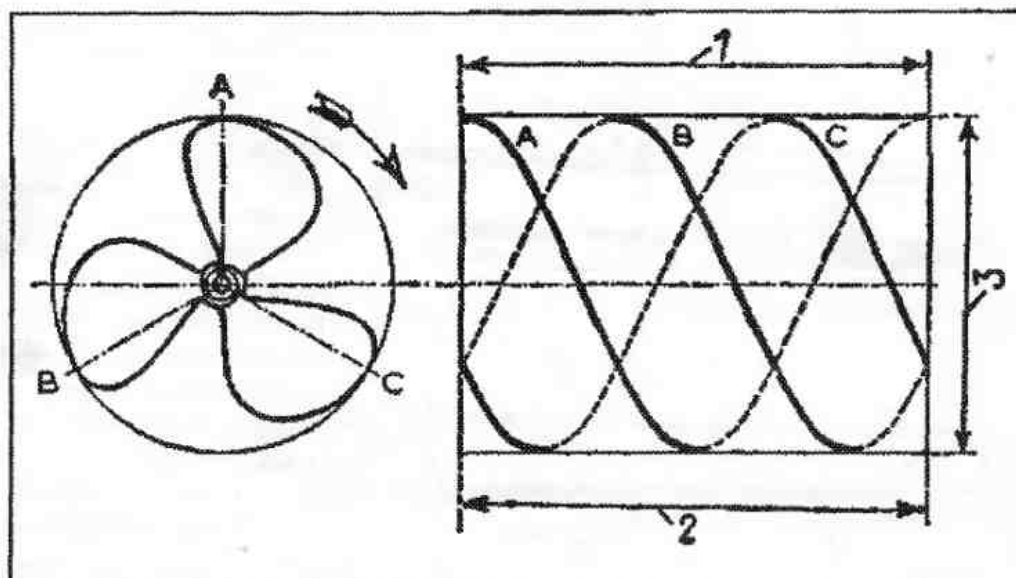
Шаг, диаметр гребного винта: 1 - один оборот; 2 - номинальный шаг; 3 - диаметр.
